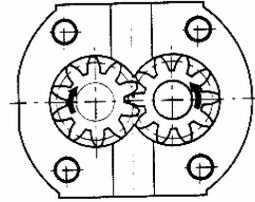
Gear Pump type PAL, R028 – 0250 secara Assembly Drawing
